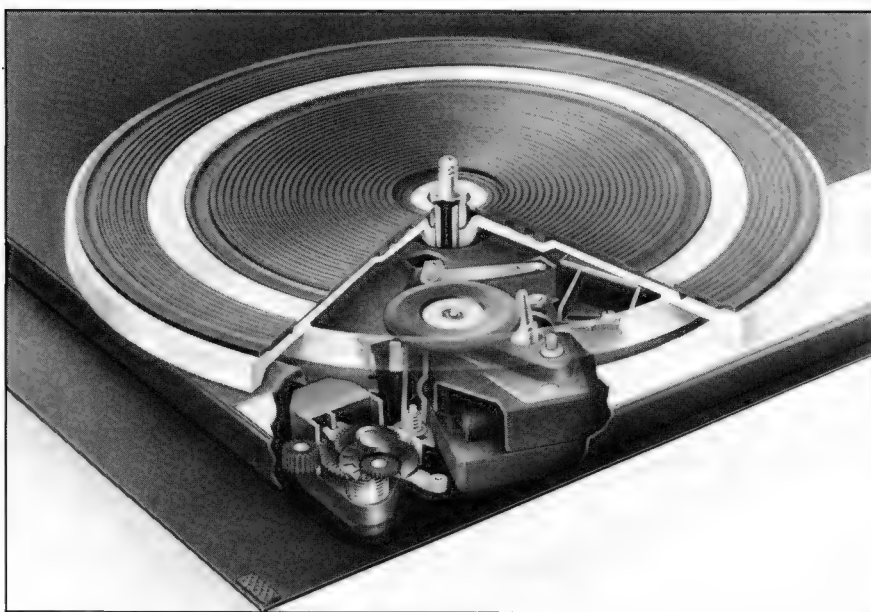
Prinzipieller Aufbau eines Plattenspielers.
